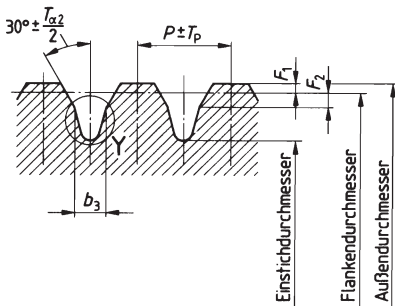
Profil mit verkürzter Flanke (Bolzensgewinde)
